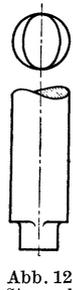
Stempelprofil kurz. Schaft von maschinell leicht herstellbarer Form.
